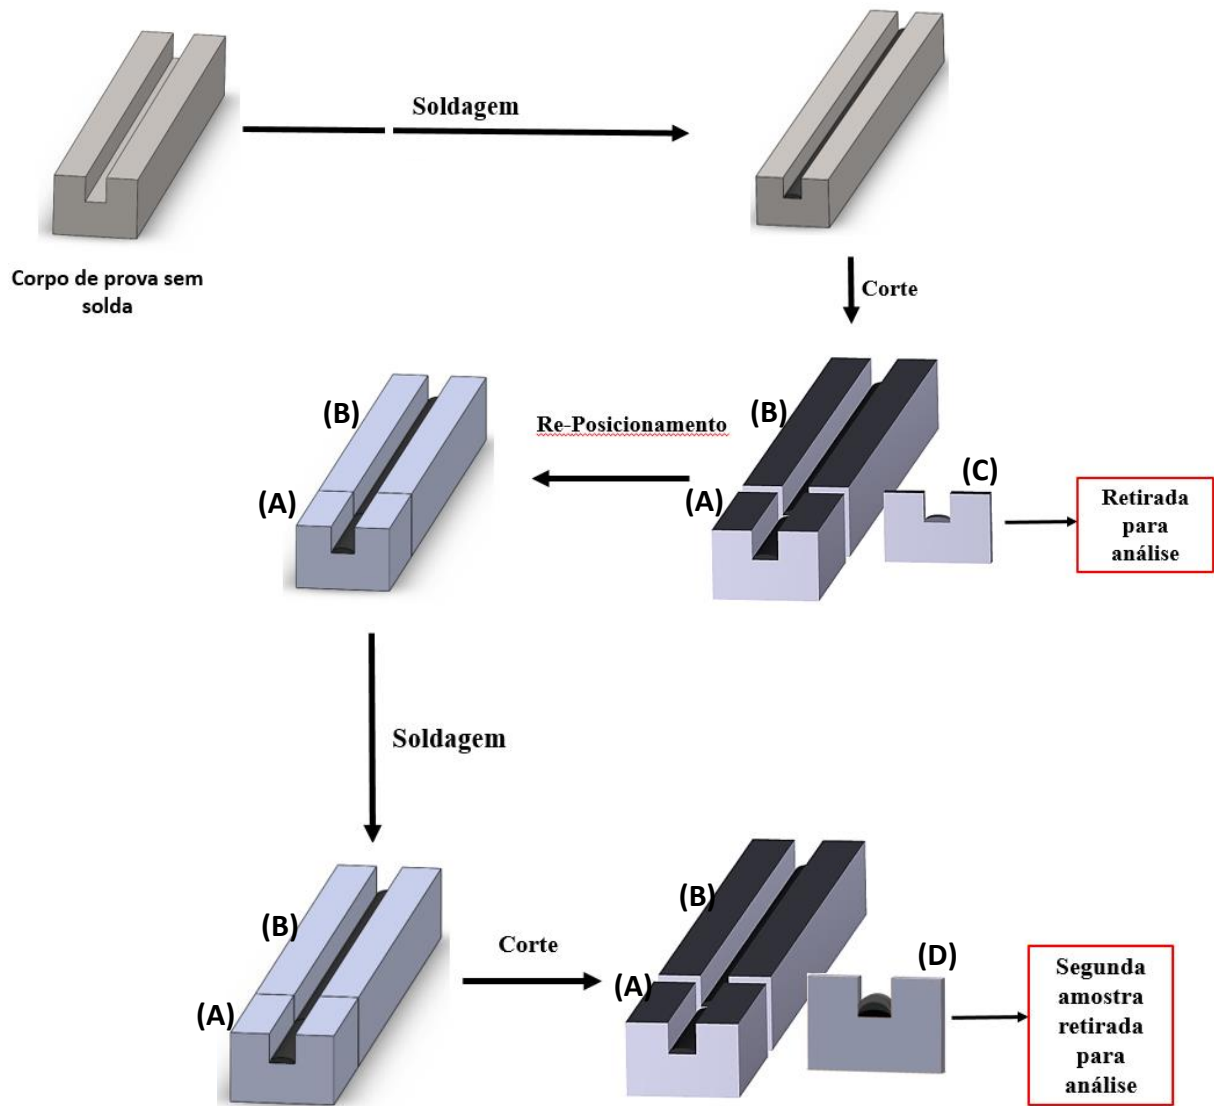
Retirada da segunda seção transversal (D) da junta soldada. Nesse momento a seção possui 2 cordões depositados.
